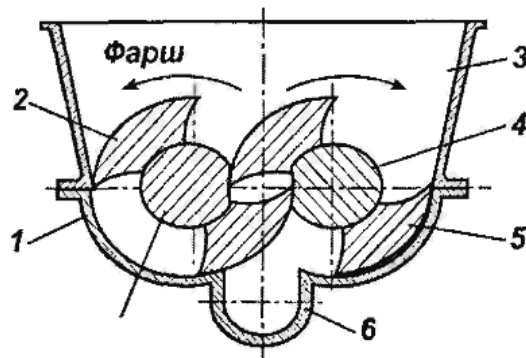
Кинематическая схема [12, 15] роторного шприца непрерывного действия: 1 - корпус; 2, 5 - роторы; 3 - бункер; 4, 7 - валы ротора; 6 – цевка
